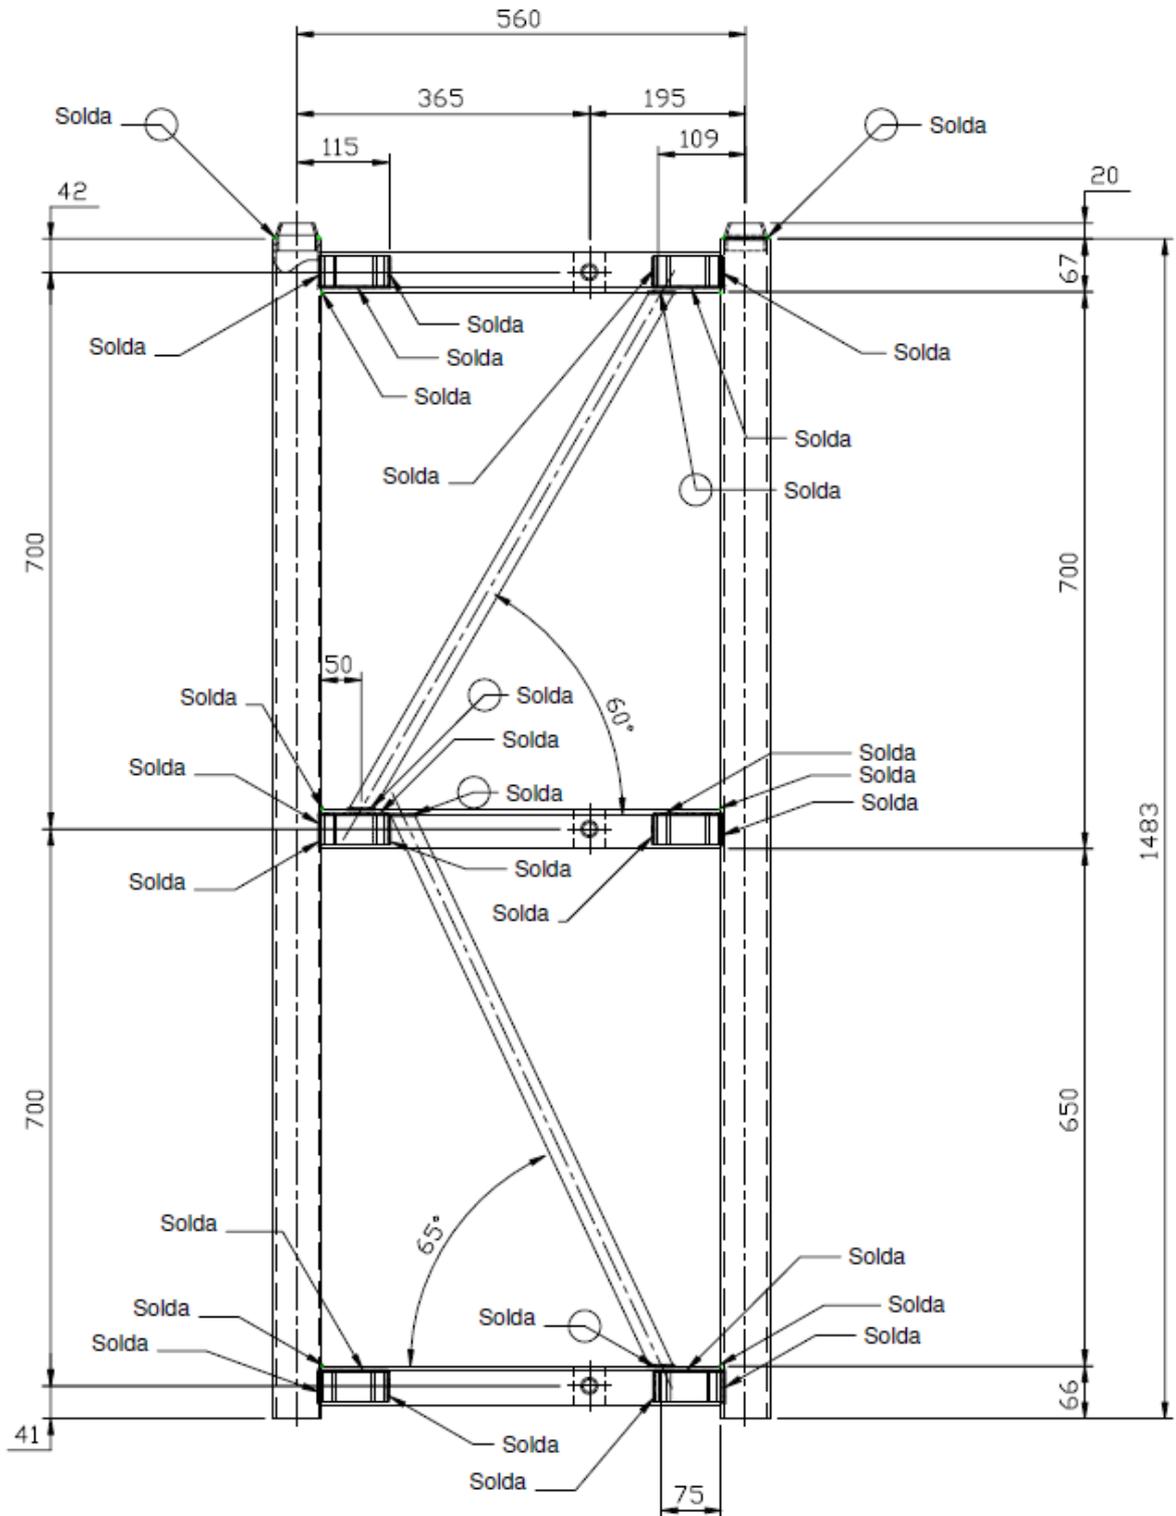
Desenho de indicação de local de solda MIG/MAG.
